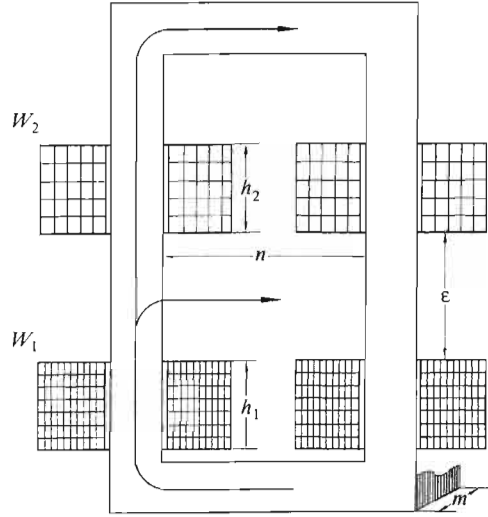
Сварочный трансформатор со стержневым магнитопроводом и подвижными обмотками
